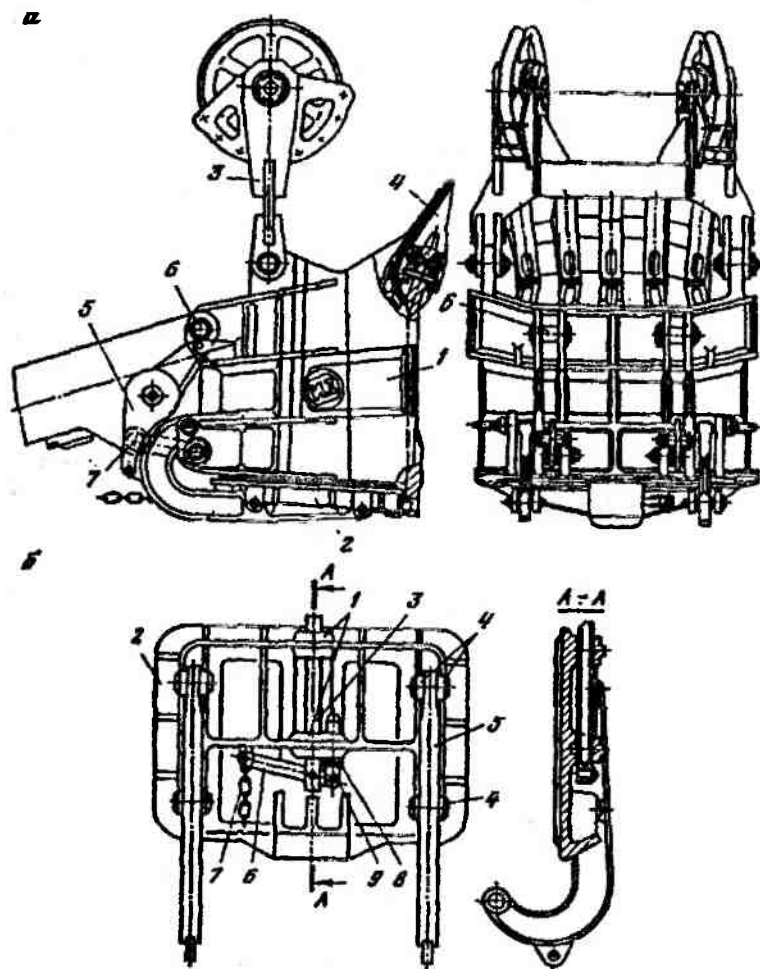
Сварно-литой ковш экскаватора:
